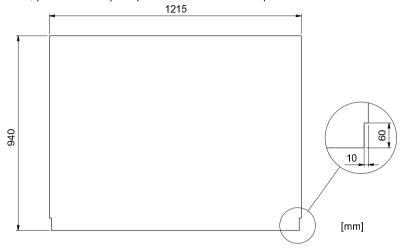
Dimensions de la planche latérale pour gravier. Remarque : des encoches sont pratiquées dans les deux angles inférieurs de la planche.
